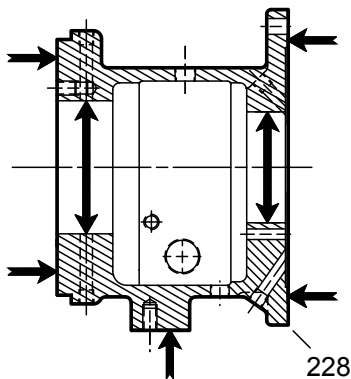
Localizações de inspeção superficial da estrutura do mancal
